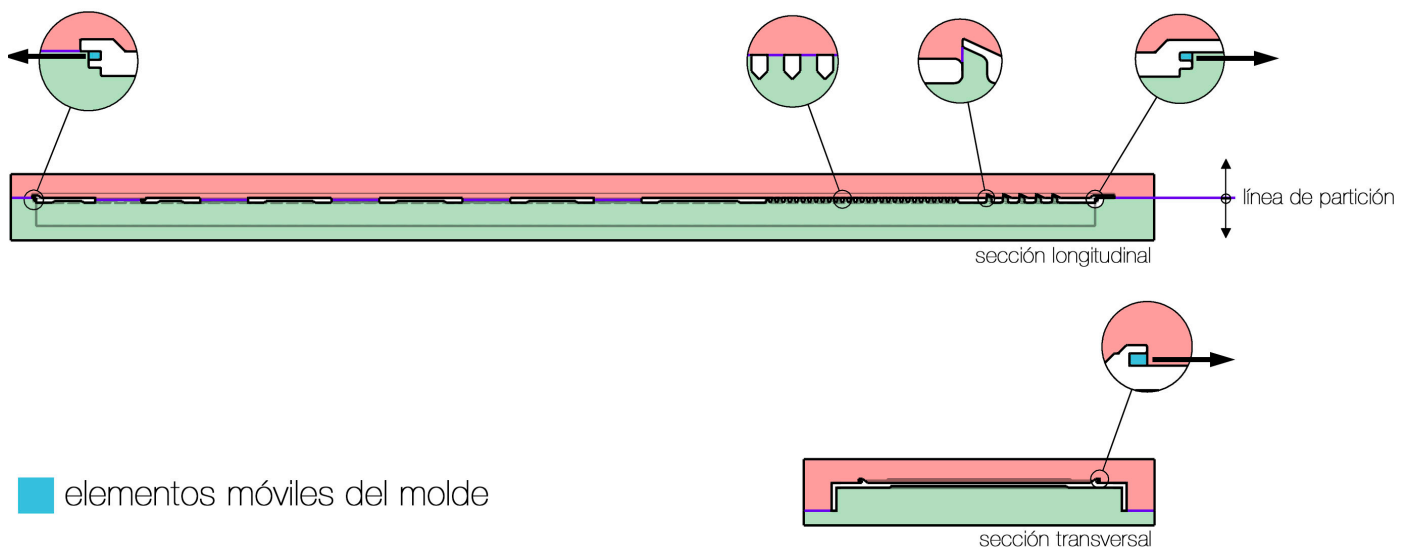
mitades molde pieza "3.- Cubierta trasera"
